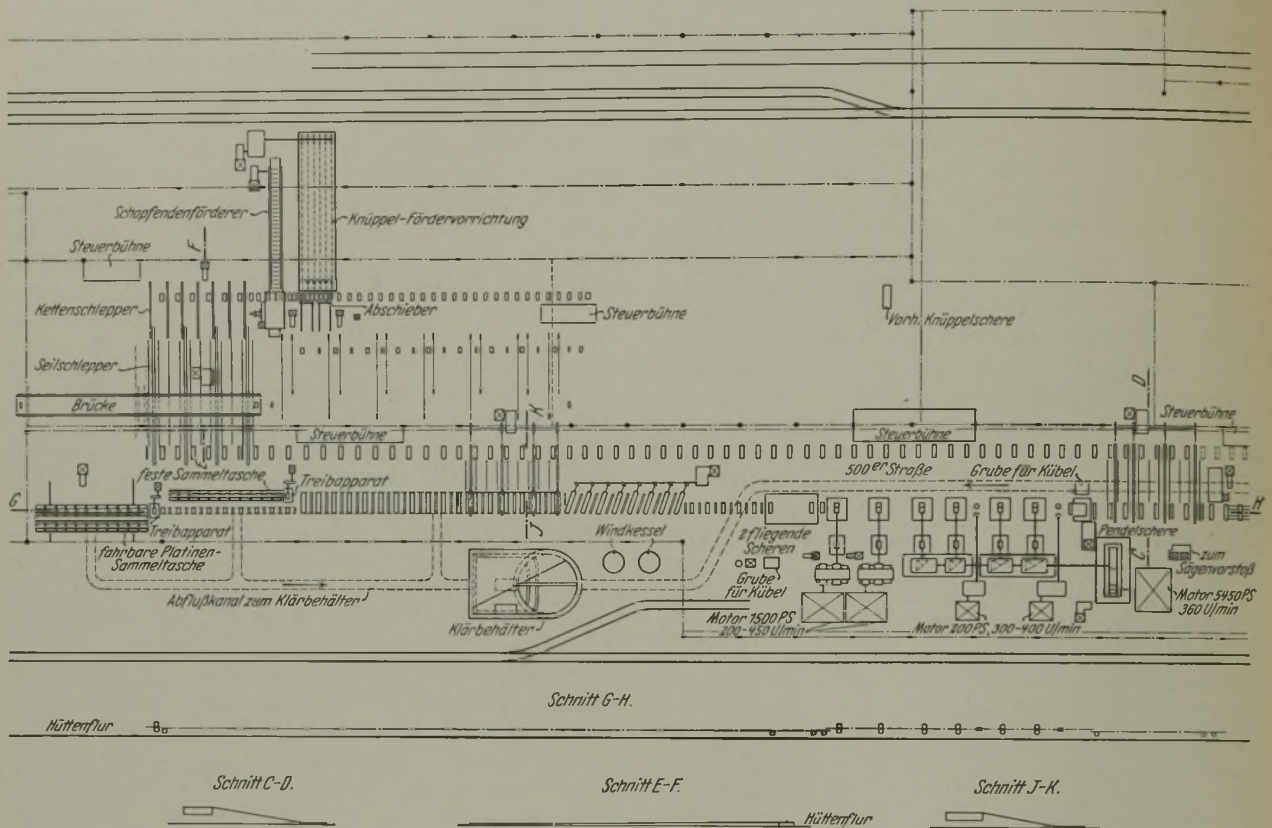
Grundriß des Knüppel- und Platinenwalzwerkes Trinec.
